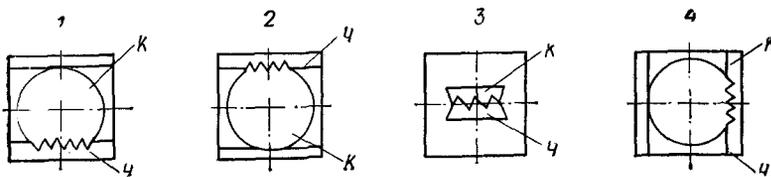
Расположение (исполнения 1—4) червячной пары:
